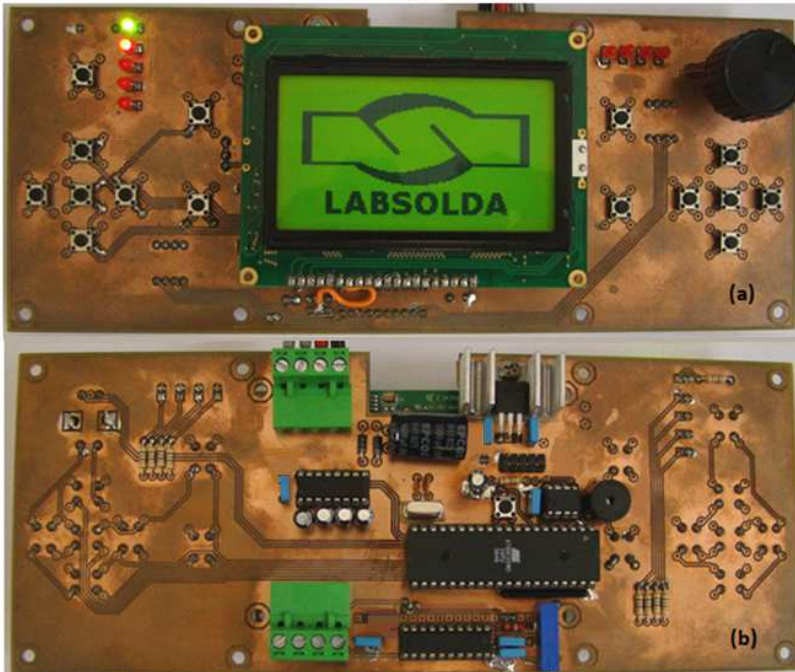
Placa eletrônica do módulo de suporte a soldagem. Em (a) a frente e em (b) o verso
